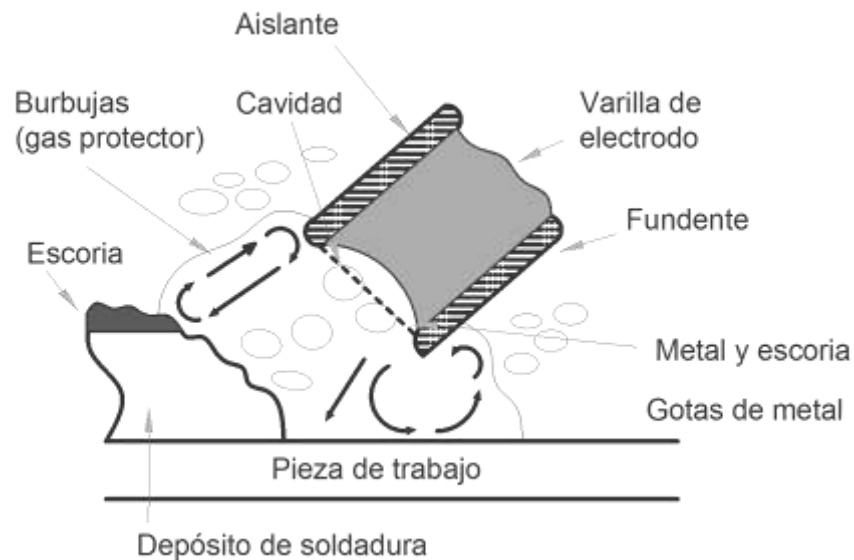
4 Esquema del proceso de soldadura húmeda MMAW (14).
